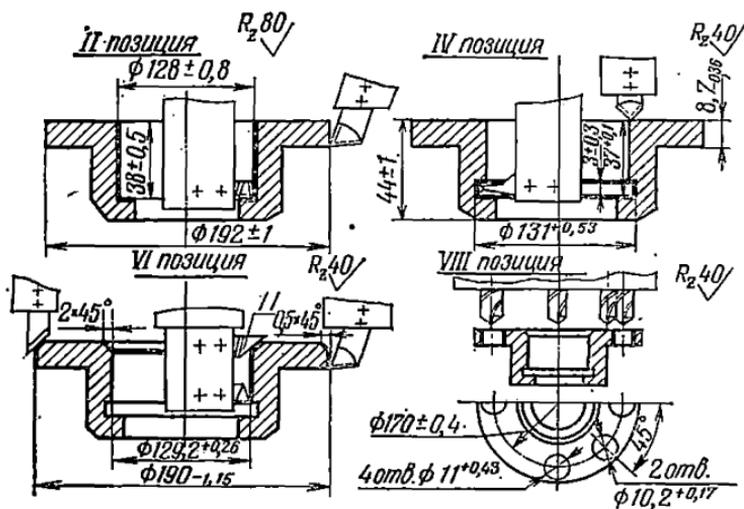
Обработка стакана роликоподшипника с установкой на II позиции.
